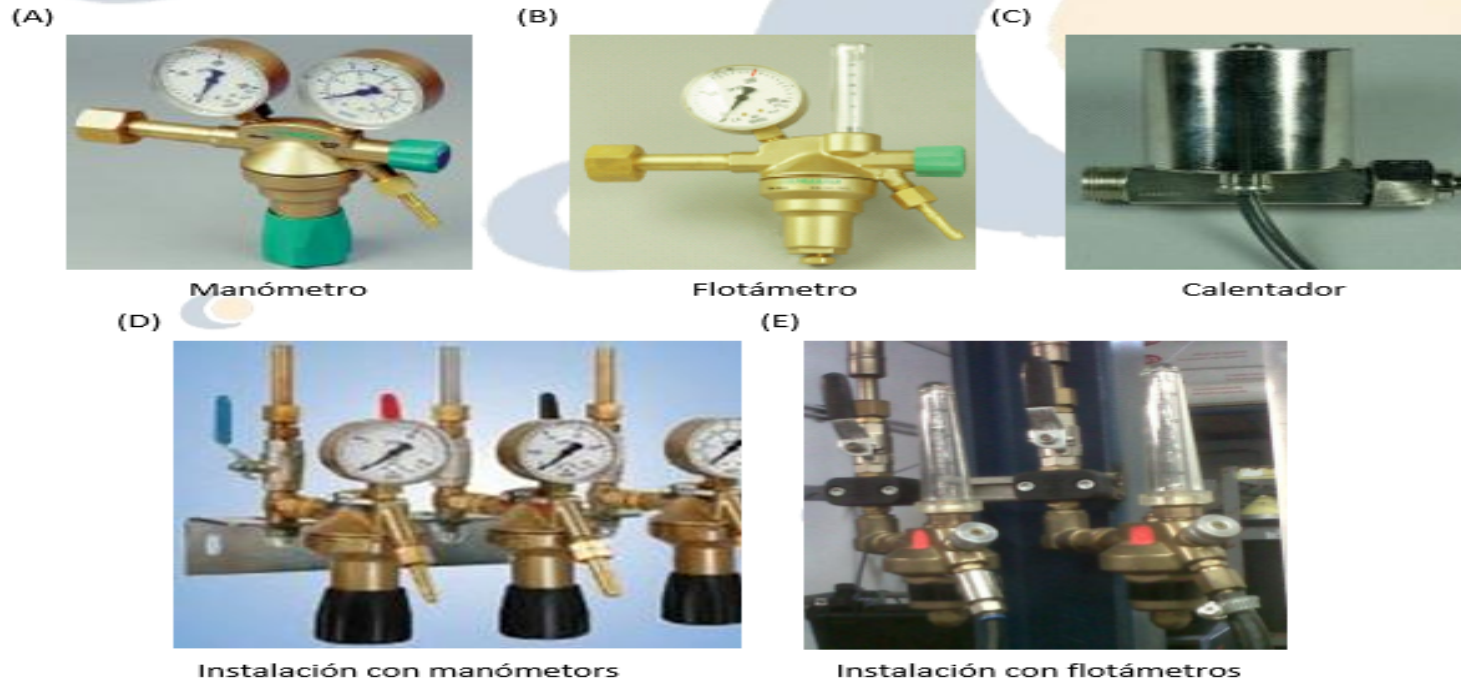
Caudalímetro con (A) manómetros y (B) con flotámetro. Puesto de trabajo (D) con manómetro y (E) con flotámetro. (C) Calentador
